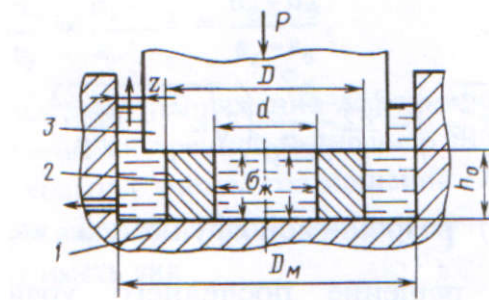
Схема роздачі з осаджуванням кільцевої заготовки
